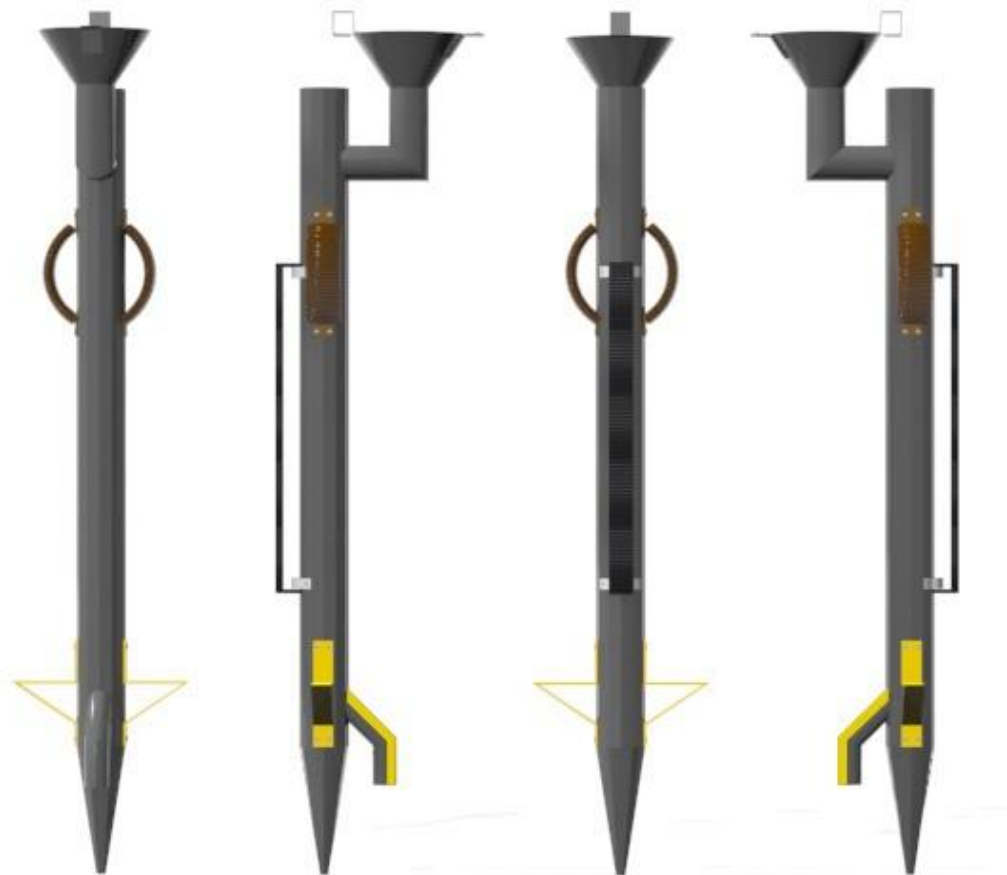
Fuente: propia - Vista frontal, laterales y posterior
